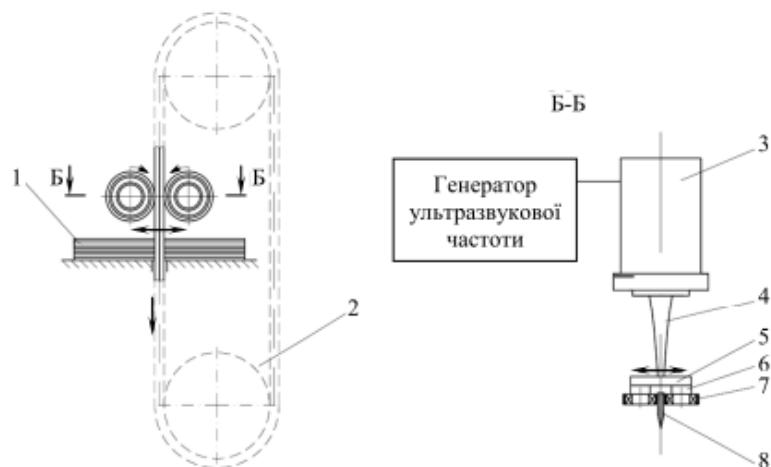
Пристрій для накладення ультразвукових коливань на стрічковий ніж розкрійної машини: 1 — настил матеріалу; 2 — механізм стрічкового ножа; 3 — збудник механічних ультразвукових коливань; 4 — акустичний трансформатор; 5 — планка; 6 — осі; 7 — вузли підшипників кочення; 8 — стрічковий ніж
